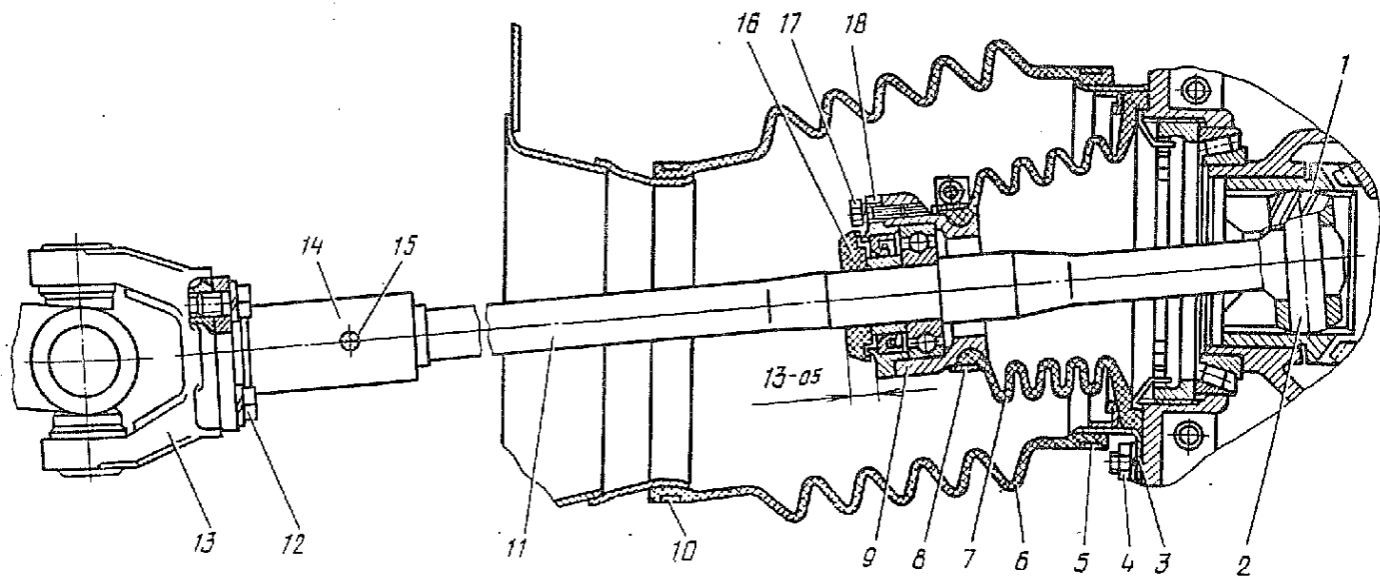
Полуось с фланцем и защитным чехлом дифференциала в сборе:
